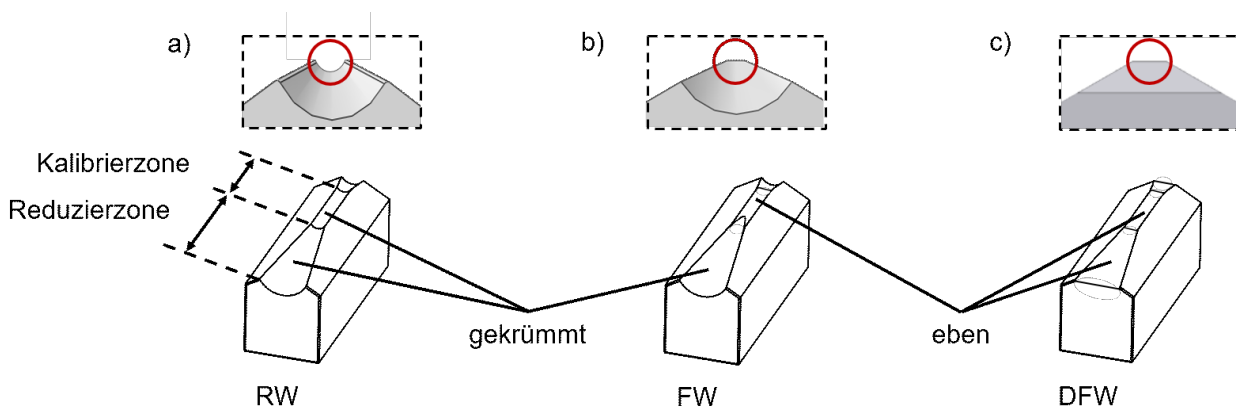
Geometrie der Rundknetwerkzeuge: a) Rundwerkzeug RW; b) Flachwerkzeug FW; c) Doppelflachwerkzeug DFW, nach [Ish20a].
